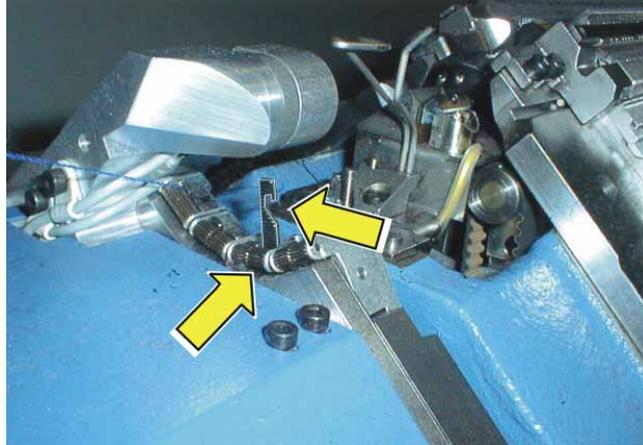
Ago di pinzatura e di taglio e pignone di serraggio
